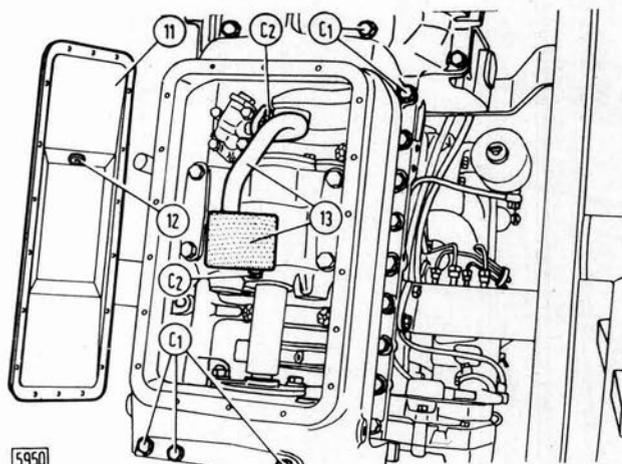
Vue du carter bassin d'huile le couvercle (11) étant déposé.
